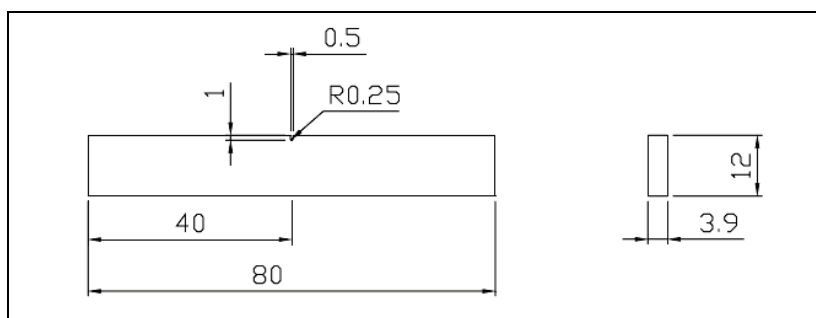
Probengeometrie der einseitig gekerbten Flachprobe (SEN-Probe) [Broll06]
